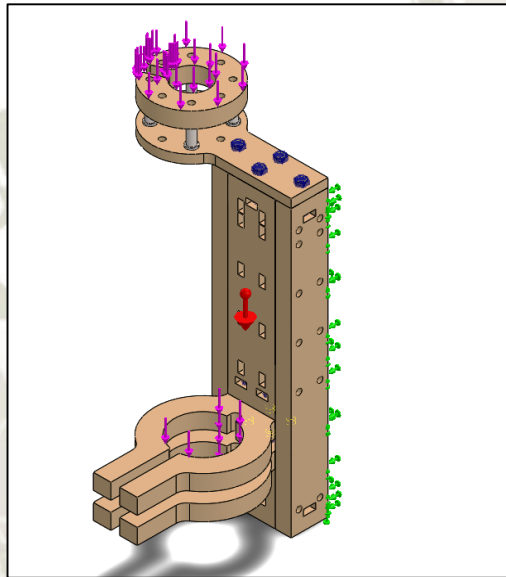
Diseño 3D – Conjunto Carro eje Z.
